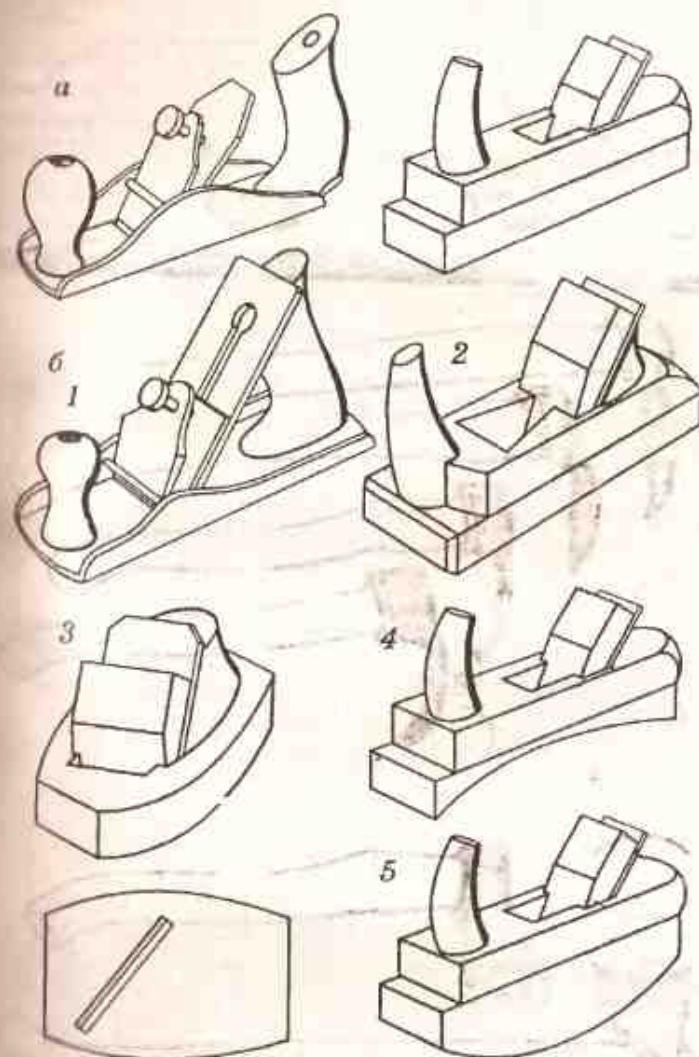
Инструменты для строгания: а — шерхебели; б — рубанки.
